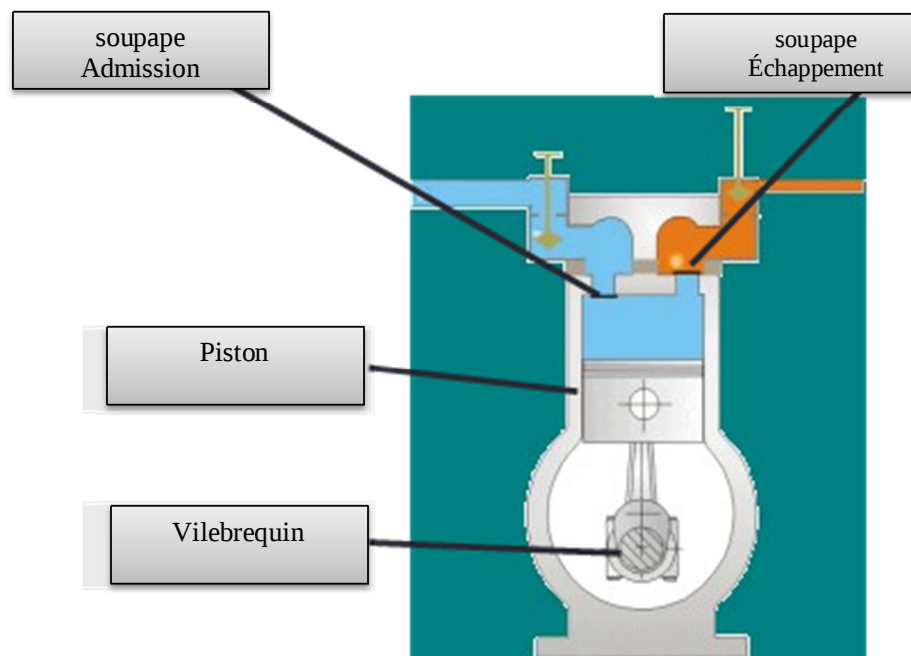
L'ensemble cylindre – piston – clapets [3]
